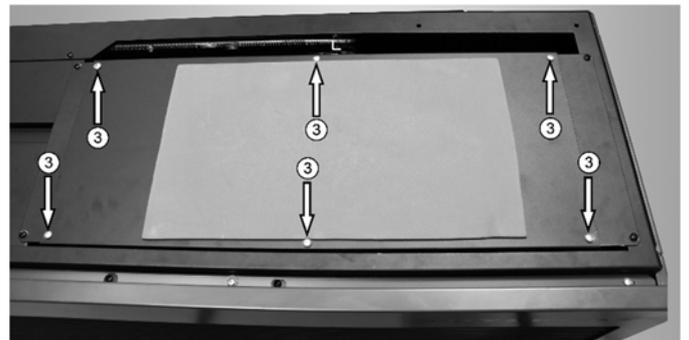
Befestigungsschrauben der Elektronikabdeckung
